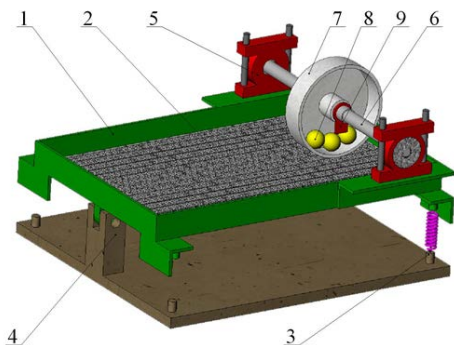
3D модель стенда грохота с колебательно-вращательным движением корпуса
